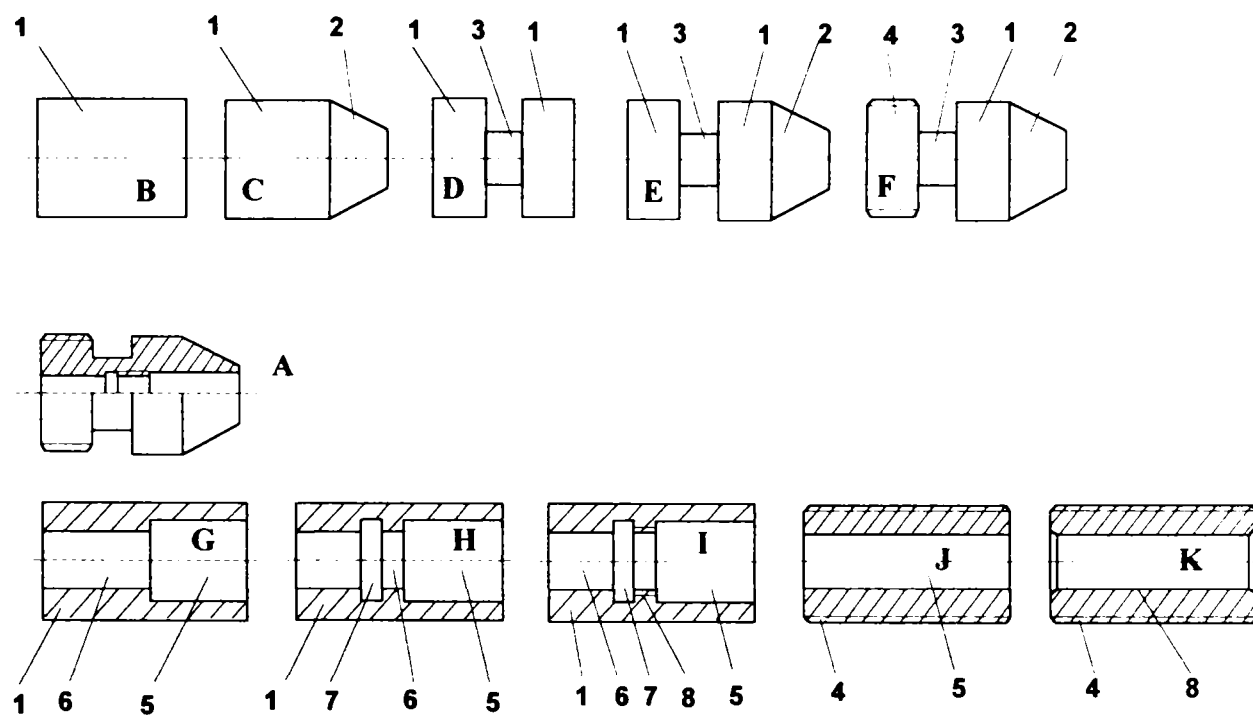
Schema cu o piesă ideală A – compusă din opt suprafețe elementare principale: 1 – cilindru exterior; 2 – con exterior; 3 – degajare exterioară; 4 – filet exterior; 5 – cilindru interior; 6 – gaură cilindrică; 7 – canal interior; 8 – filet interior; B,C,D etc. – piese concrete, compuse din același fel de elemente geometrice, dar combinate diferit.
